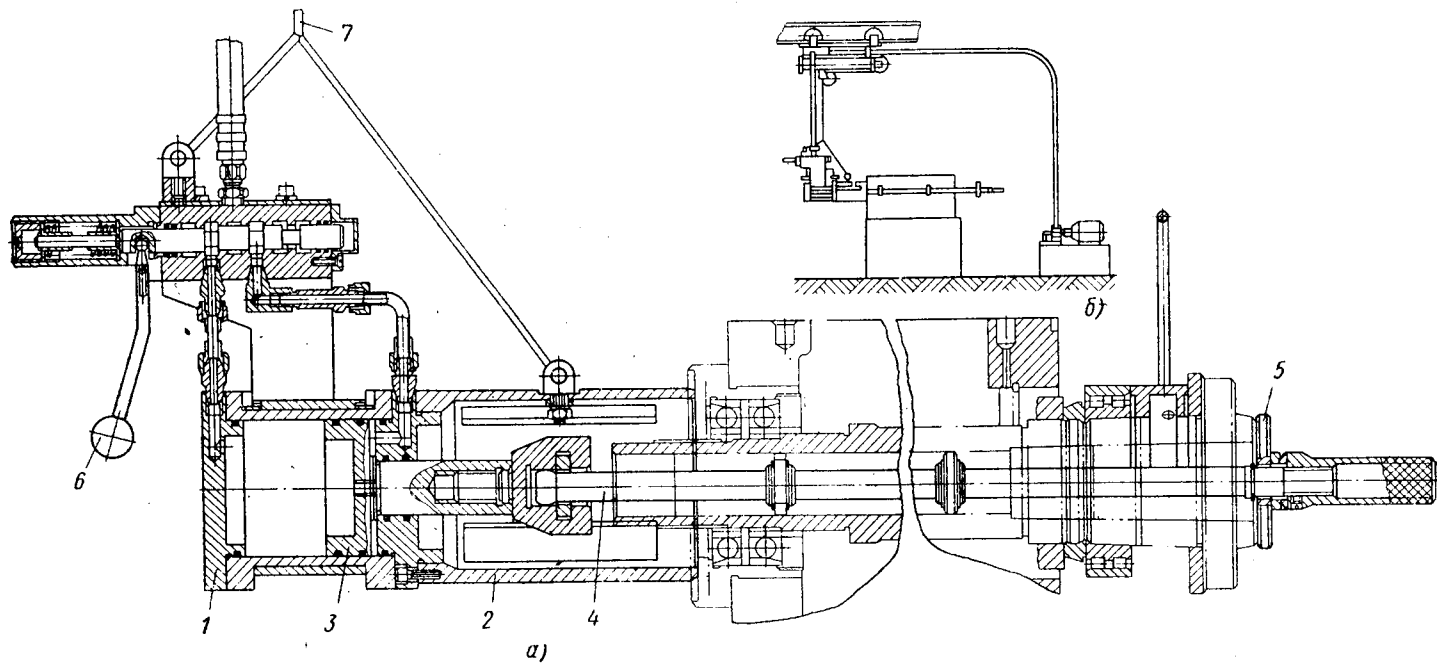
Приспособление для запрессовки шпинделя в корпус:
